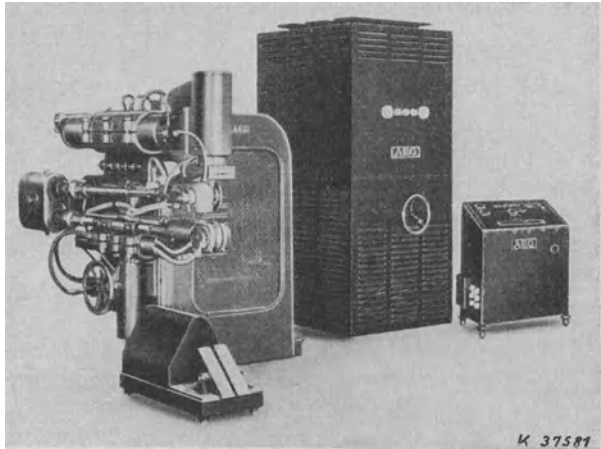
Elektrische Nahtschweißmaschine für zweistufige Stromsteuerung.
